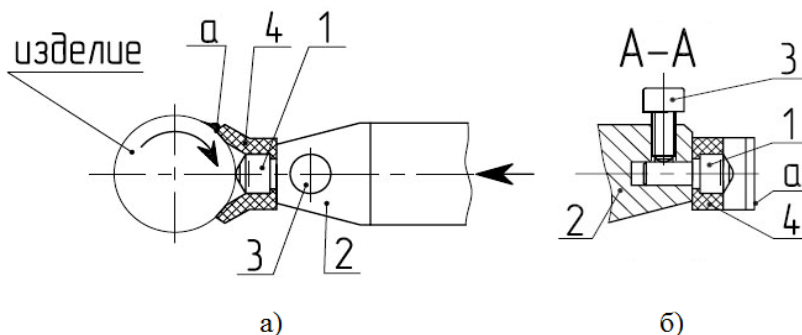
Рабочая зона инструмента: а) рабочая часть устройства; б) крепление грязесъемника; 1 — индентор; 2 — державка; 3 — винт; 4 — грязесъемник; а — прямолинейная кромка
